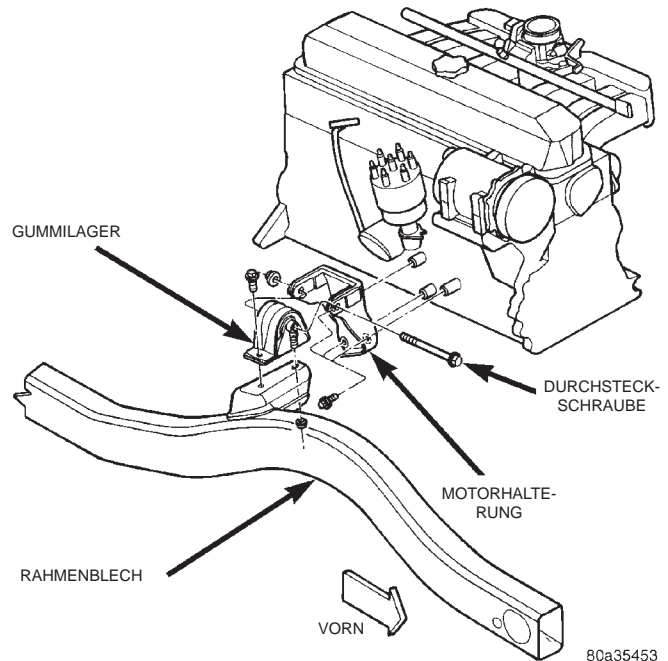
Motoraufhängung vorne rechts—4.0L-Motor
